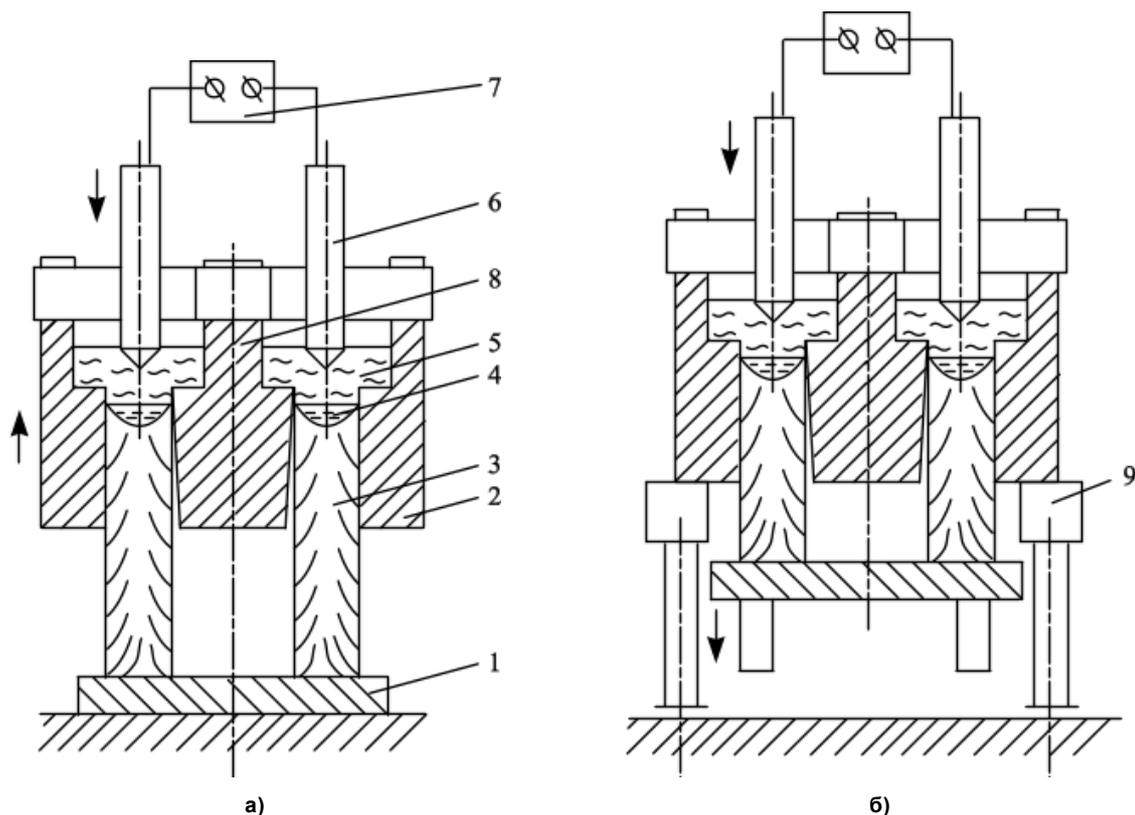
Схемы ЭШП с перемещением кристаллизаторов и полых заготовок: а – с неподвижной заготовкой и перемещающимся вверх блоком кристаллизаторов; б – с неподвижным блоком кристаллизаторов и перемещающейся вниз выплавляемой заготовкой; 1 – поддон; 2 – наружный кристаллизатор; 3 – заготовка; 4 – металлическая ванна; 5 – шлаковая ванна; 6 – расходующий электрод; 7 – источник питания; 8 – дорн, соединенный в блок с наружным кристаллизатором; 9 – платформа для кристаллизатора
